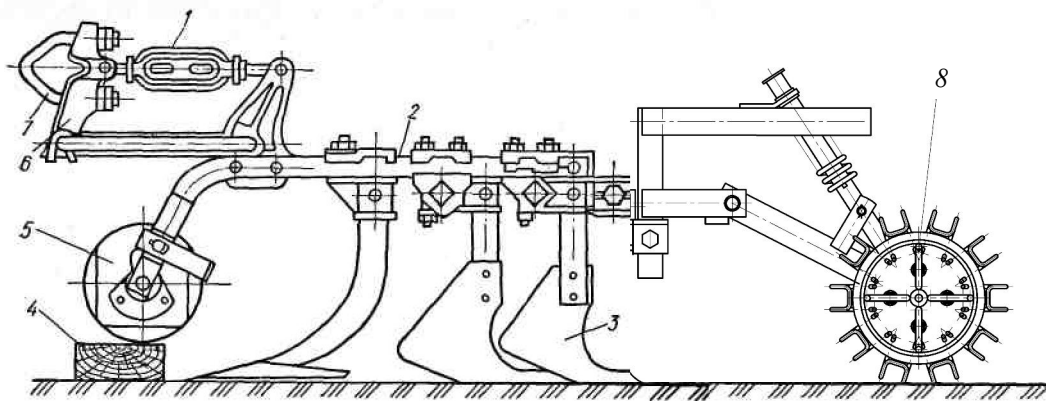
Регулювання секції робочих органів культиватора ALTAIR-5,6: 1 - регулювальна гайка; 2 - гряділь; 3 - робочий орган; 4 - брусок; 5 - колесо; 6 - кронштейн; 7 - скоба; 8 - борінка
